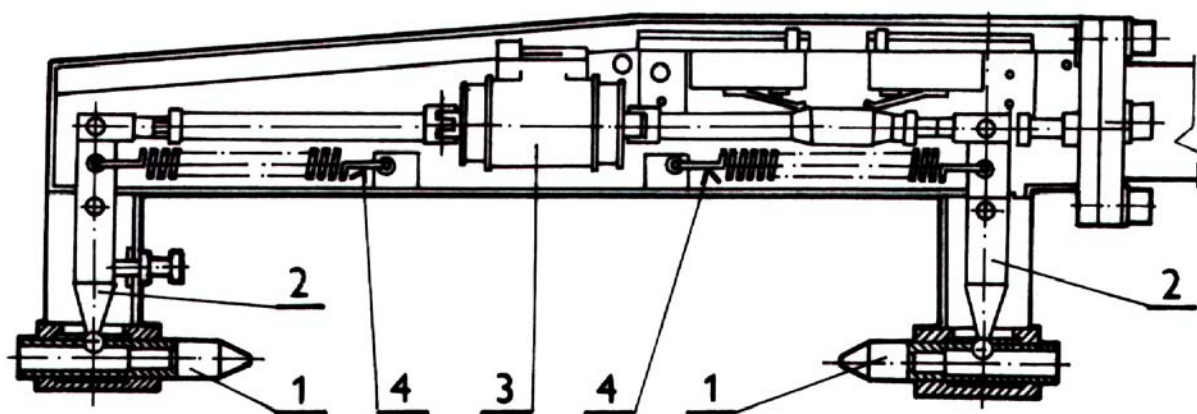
3 Pasivní mechanický efektor s pružinou
